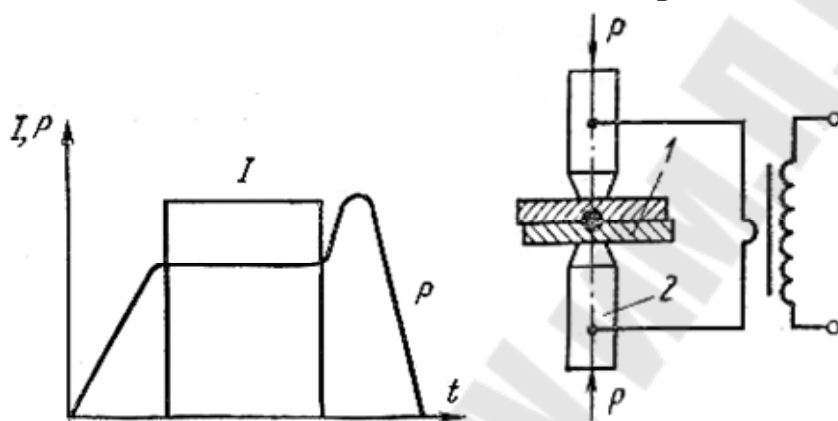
Циклограмма и схема контактной точечной сварки
